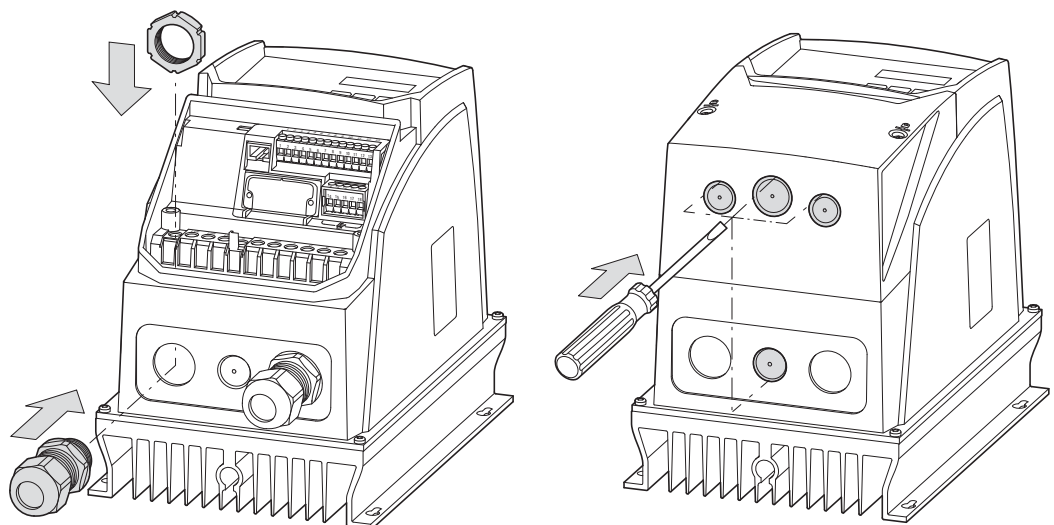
Kabeldurchführungen für Verschraubungen in Schutzart IP66
